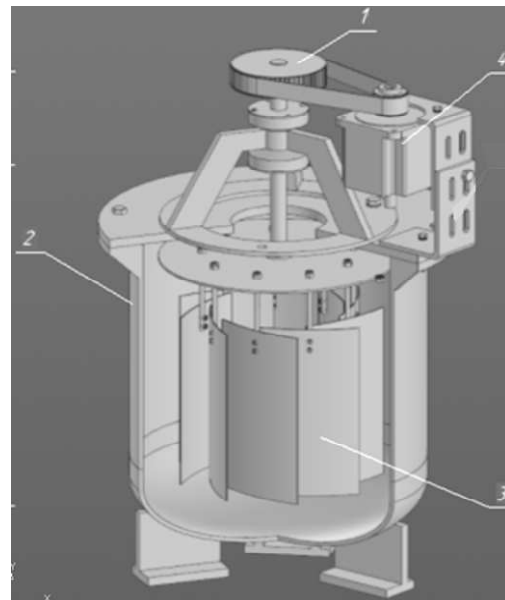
Конструктивная схема лабораторного волнового смесителя: 1 – узел преобразования движения (привод колебаний); 2 – корпус (рабочая ёмкость); 3 – мешалка; 4 – шаговый электродвигатель
